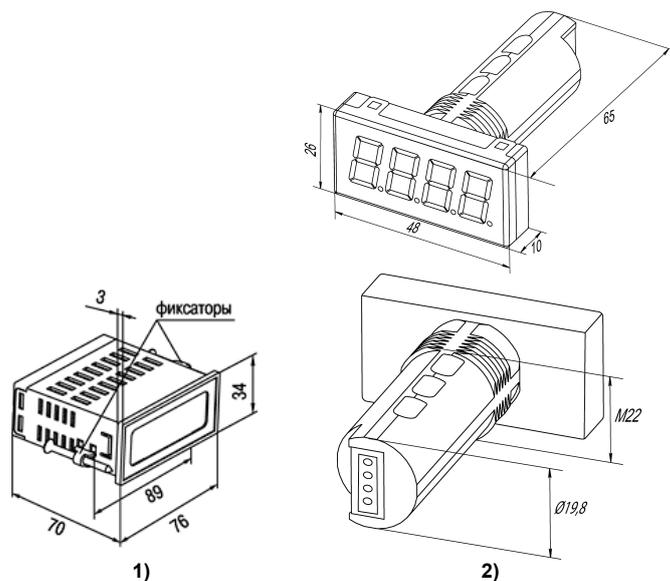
Габаритный чертеж прибора в корпусе ЩЗ (1) и Щ9 (2)
